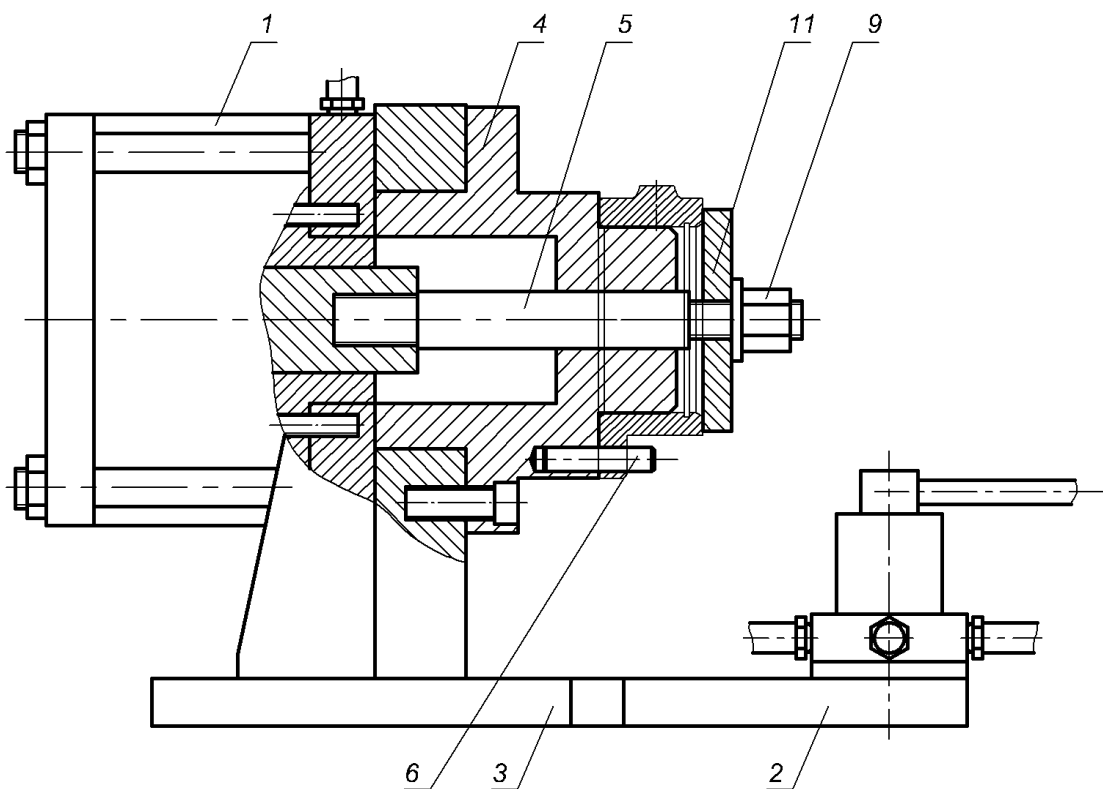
Пристрій для фрезерування площини у деталі
